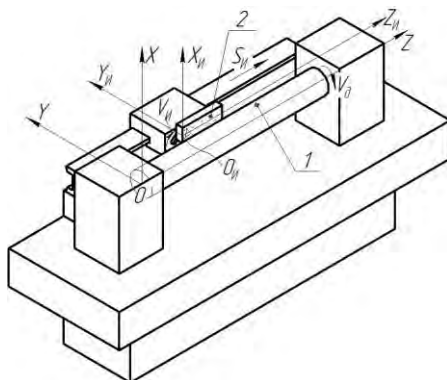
Модель обробки циліндричної голчастої поверхні торцем бруска
